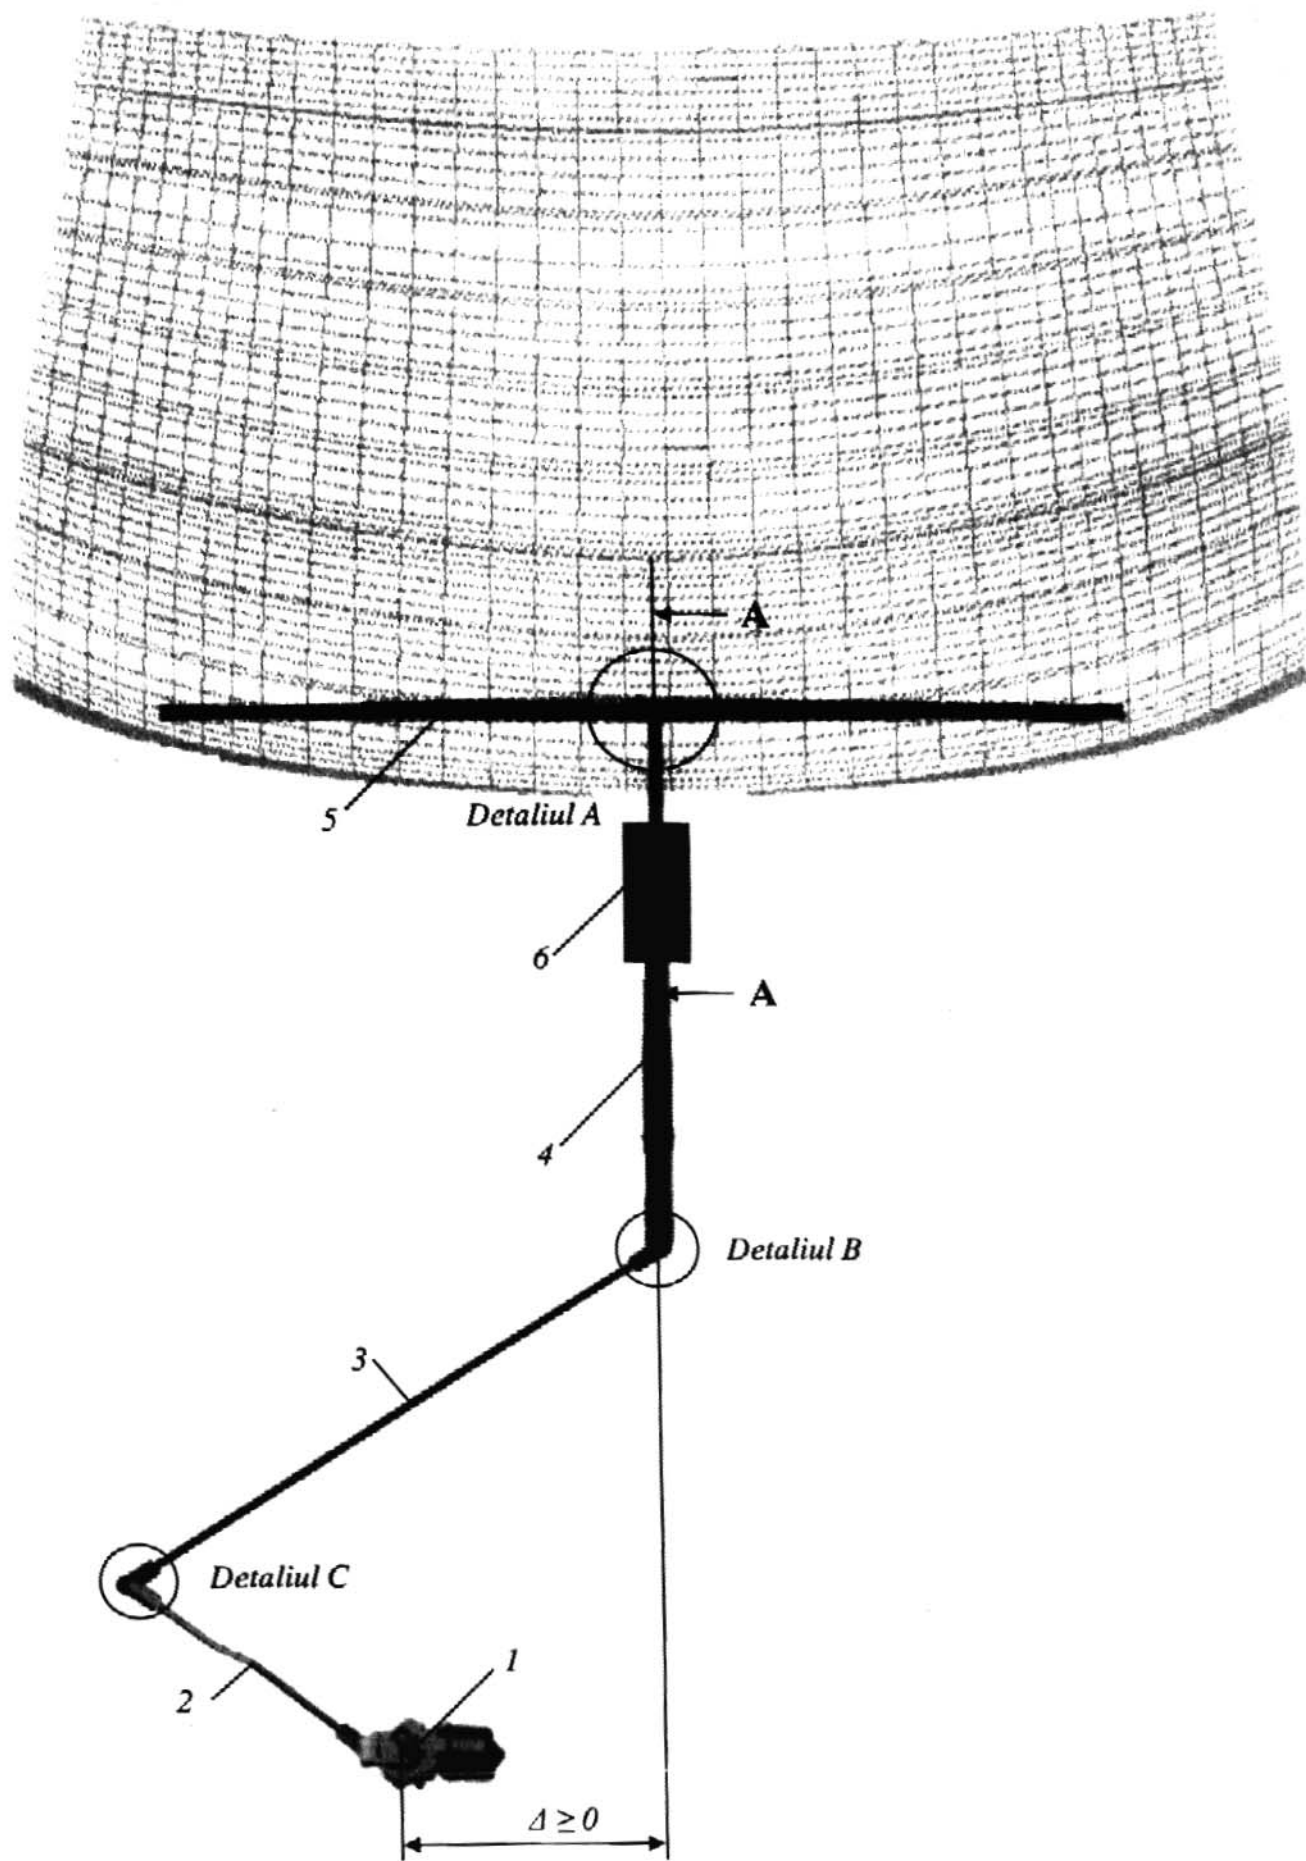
Mecanism ștergător cu deplasare plan paralelă
